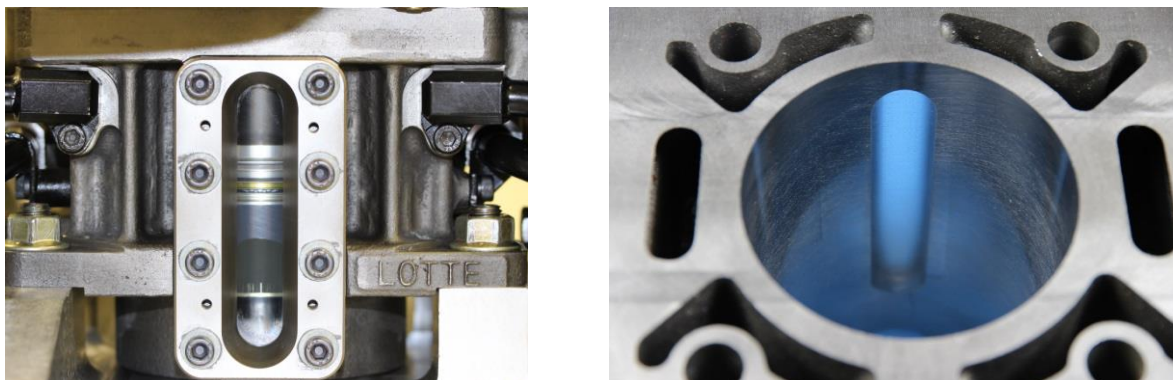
Optischer Zugang der Zylinderbuchse auf der Druckseite. Links: Außenaufnahme im eingebauten Zustand mit Kolben. Rechts: Innenansicht mit ausgebautem Kolben.
